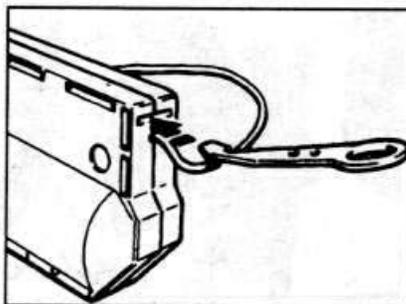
Установка скобы на пружинный механизм автоматического натяжения ремня.
